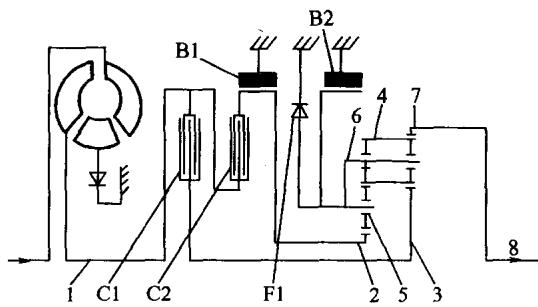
7 拉维尼克斯式三挡行星齿轮变速器结构简图
